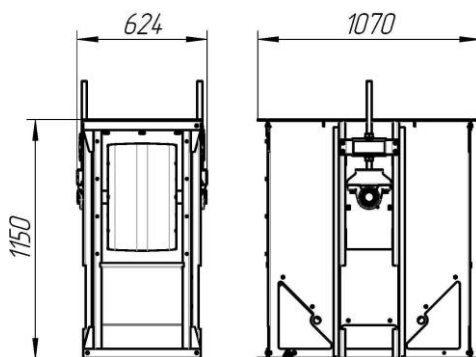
Станция натяжная нории Н-100. Размеры габаритные
